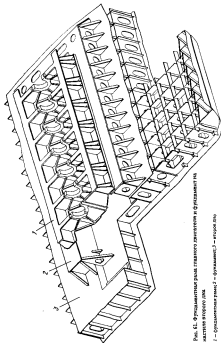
Фундаментная рама главного двигателя и фундамент на машинном втором деке.
